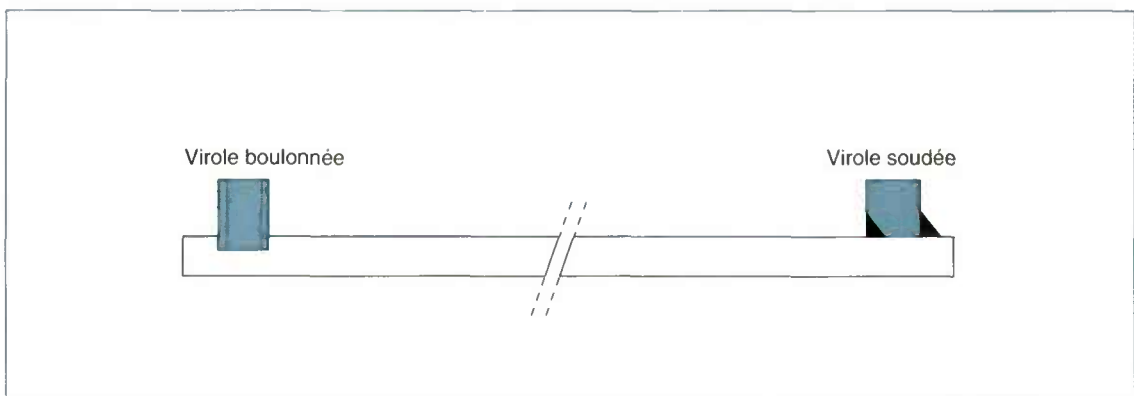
Modèles de virole boulonnée ou soudée.
